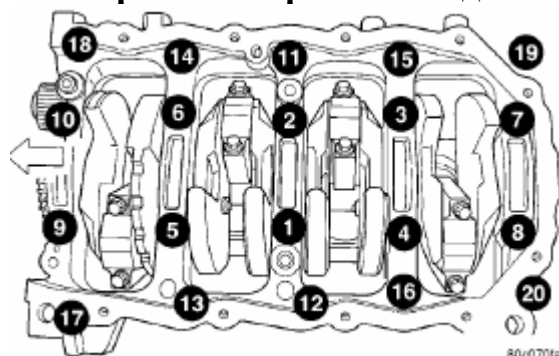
Порядок затяжки болтов крышек коренных подшипников/основания.
